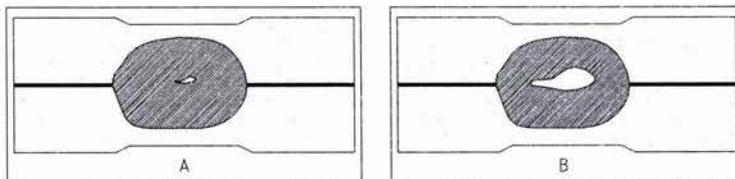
Cavidades internas en el punto de soldadura: (A) pequeña y (B) Larga.
